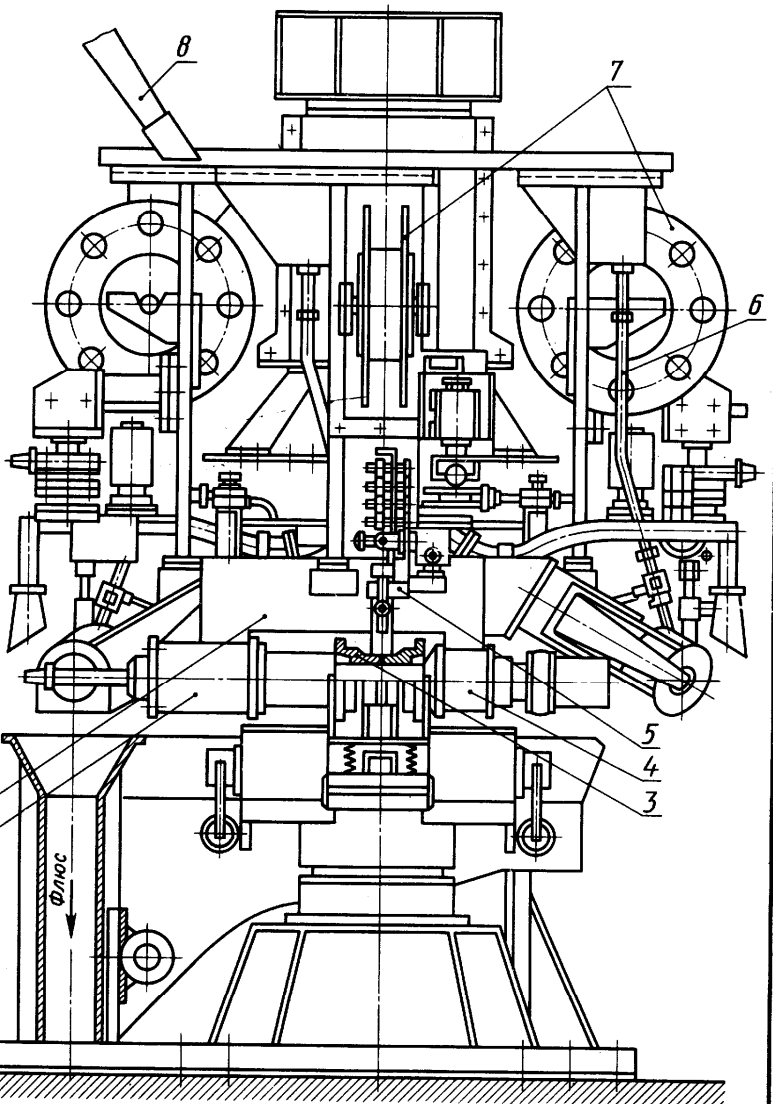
Станок-автомат роторного типа для сборки и сварки катков трактора
